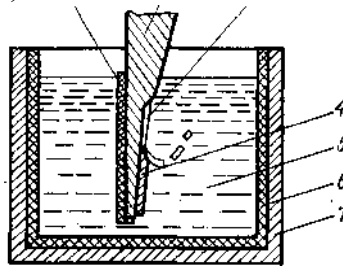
Схема нарощування леза лемеша розплавом твердого сплаву: 1 — ізоляція; 2 — лезо; 3 — розплавлений флюс; 4 — нарощений шар; 5 — розплав твердого сплаву; 6 — вогнетривка ізоляція ванни; 7 — ванна.
